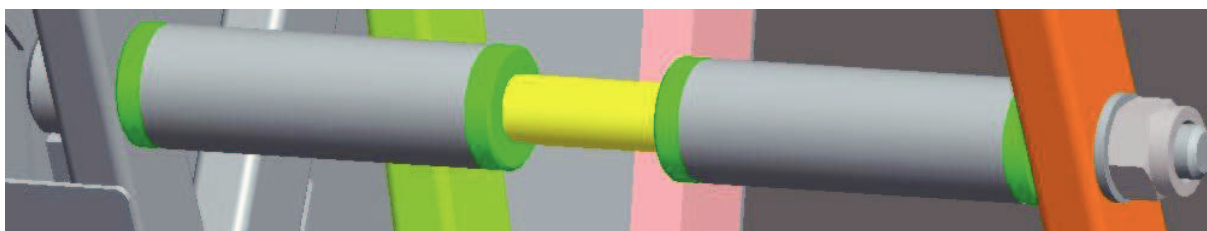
Úchyt pro zadní část motoru č. 1
